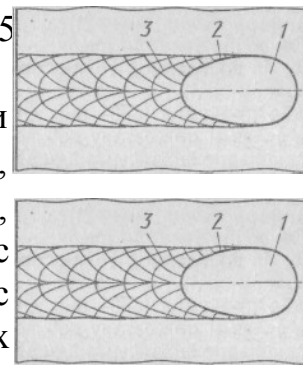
Столбчатые кристаллиты в сварном шве: 1 – сварочная ванна; 2 – изотерма кристаллизации шва; 3 – столбчатый кристаллит
